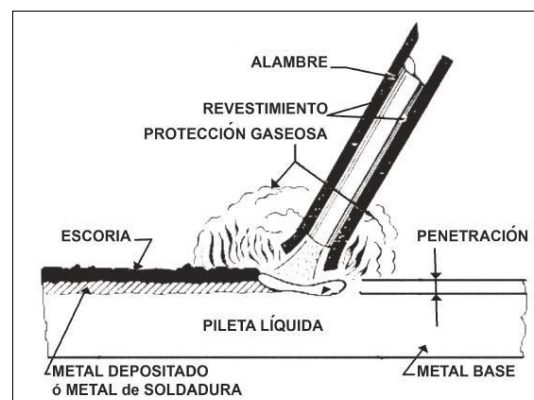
Esquema de soldadura SMAW [24]
